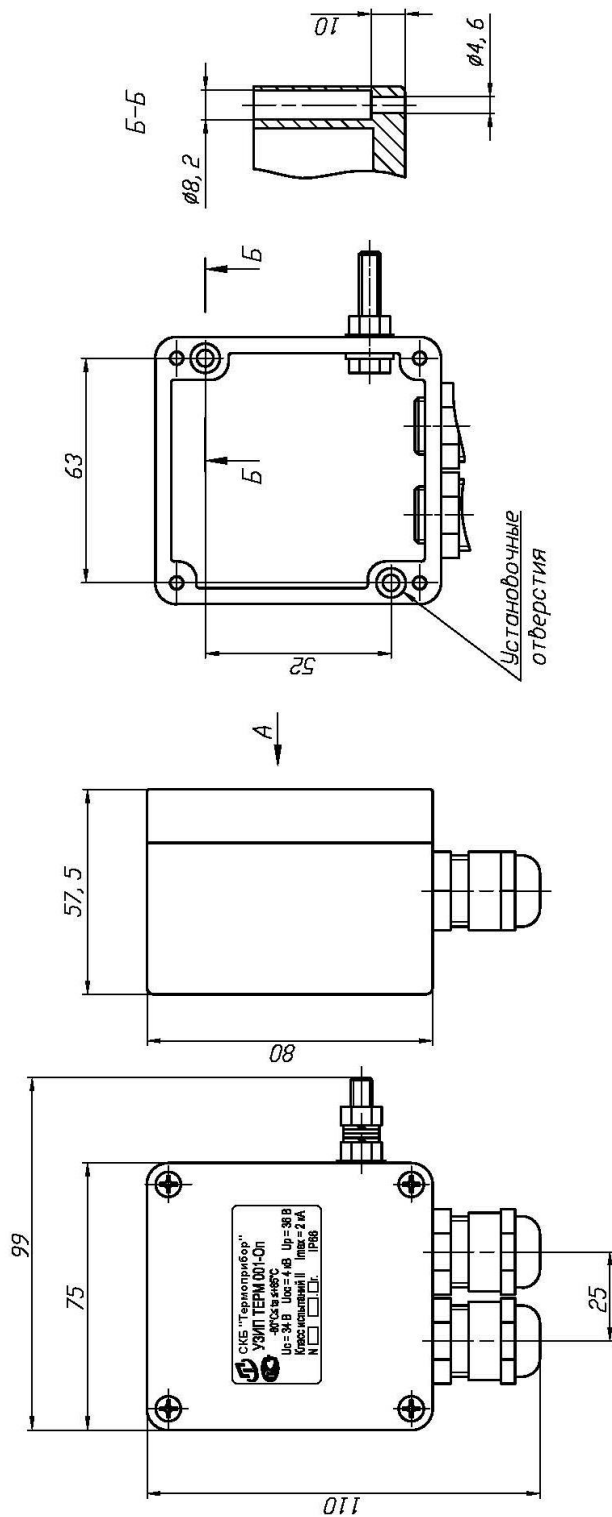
Габаритный чертеж УЗИП ТЕРМ 001 с корпусом типа «КС1»
